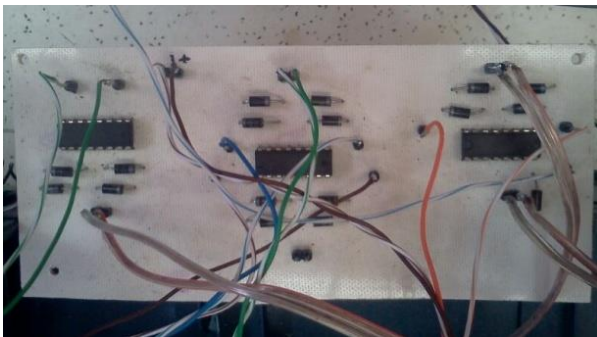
Fotografía de la parte frontal de la placa de los drivers
